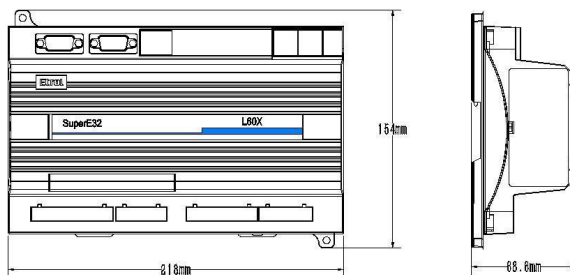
SuperE32 L606 RTU 模块外形尺寸
